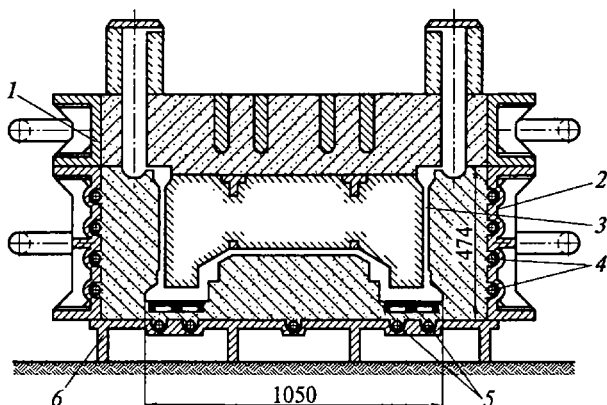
Конструкция оснастки для охлаждения отливок:
